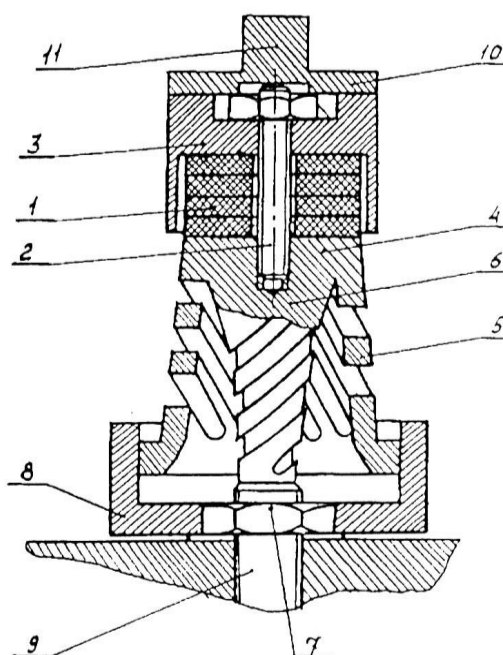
Спосіб розбирання різьбових з'єднань: 1- п'єзокерамічний перетворювач; 2- шпилька; 3- корпус; 4- частотнопонижувальний елемент разом з торсіоном 5 і коцентратором 6; 7- відгвинчувальна гайка; 8- наконечник; 9- болт; 10, 11- перехідник і квадрат.
